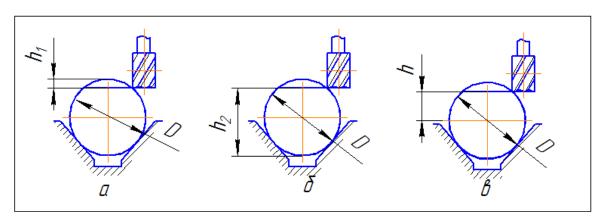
Схемы установки вала на призму для фрезерования поперечного паза Из геометрических построений находим:
